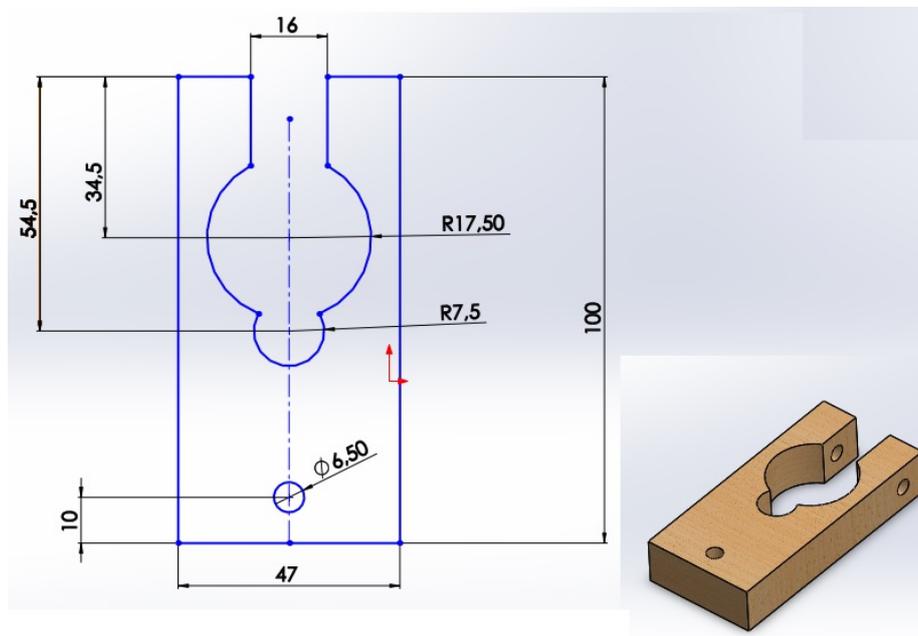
desenho técnico para auxiliar na construção do componente 11: suporte para o motor.
